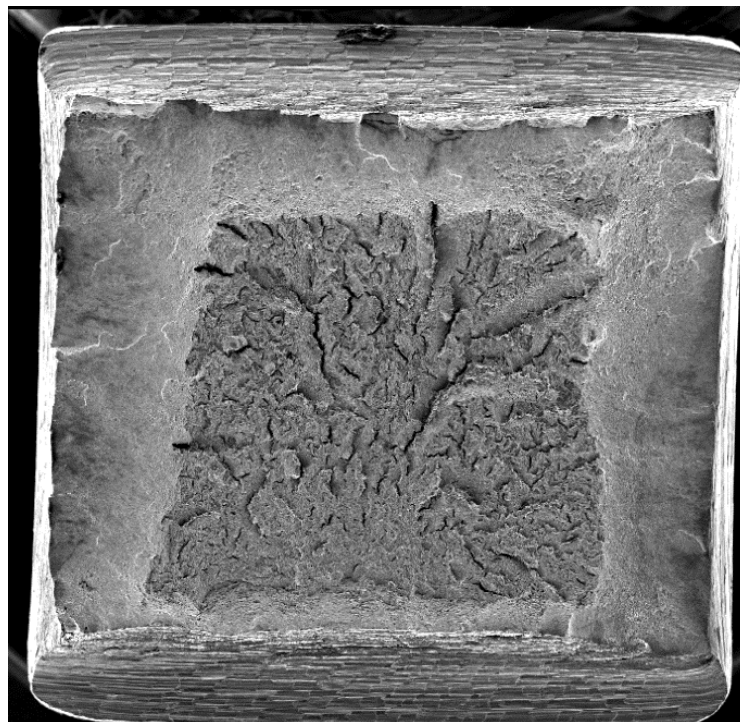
Superficie de fractura de la probeta B4-CC-1.
